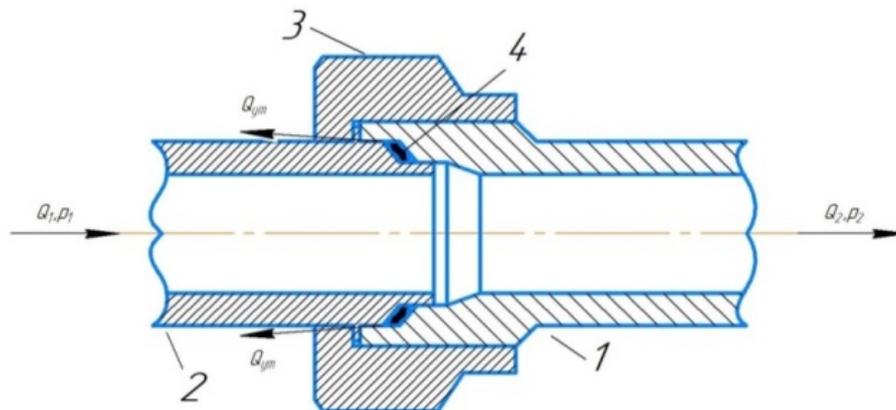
Схема утечек РЖ на стыке трубопроводов:
